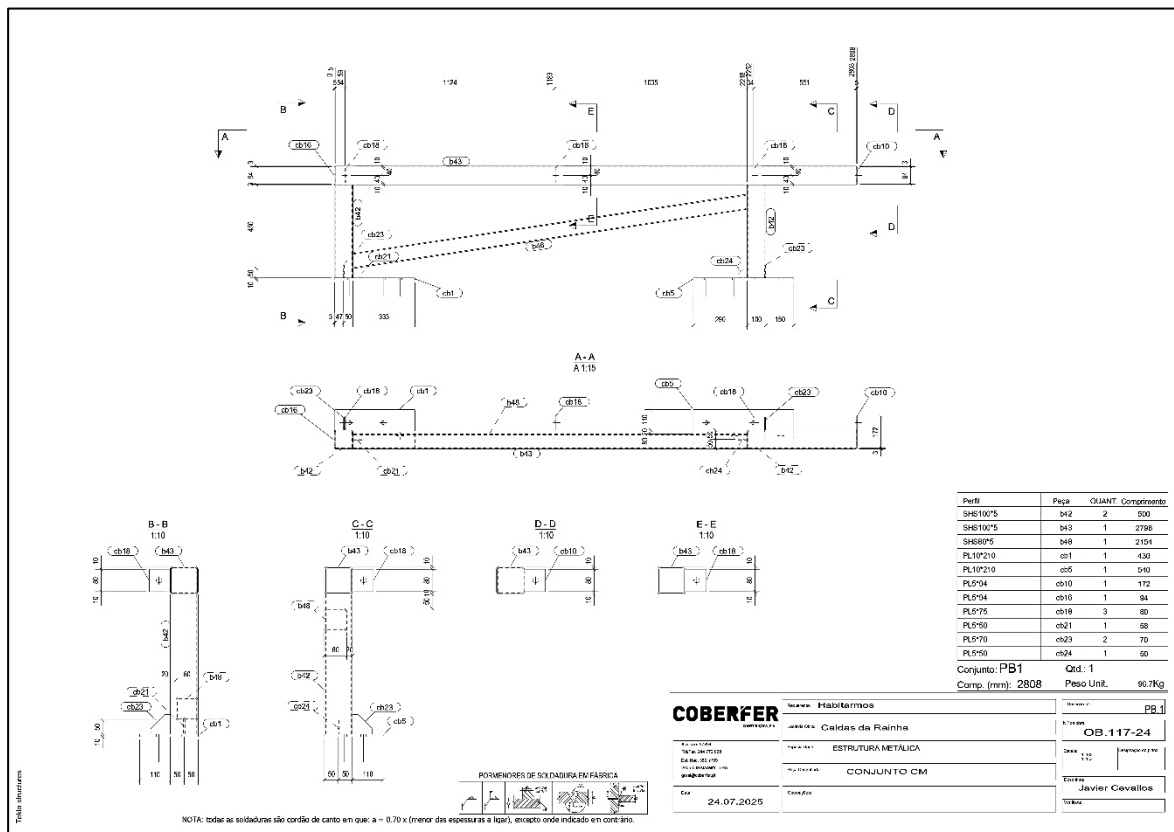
Desenho de conjunto “PB1” da OB.117-24 (Autor/Coberfer)
